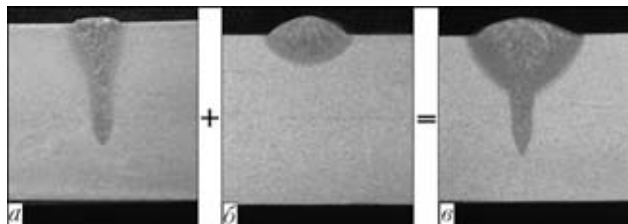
Макрошлифы швов, выполненных лазерной (а), дуговой (б) и лазерно-дуговой (в) сваркой
